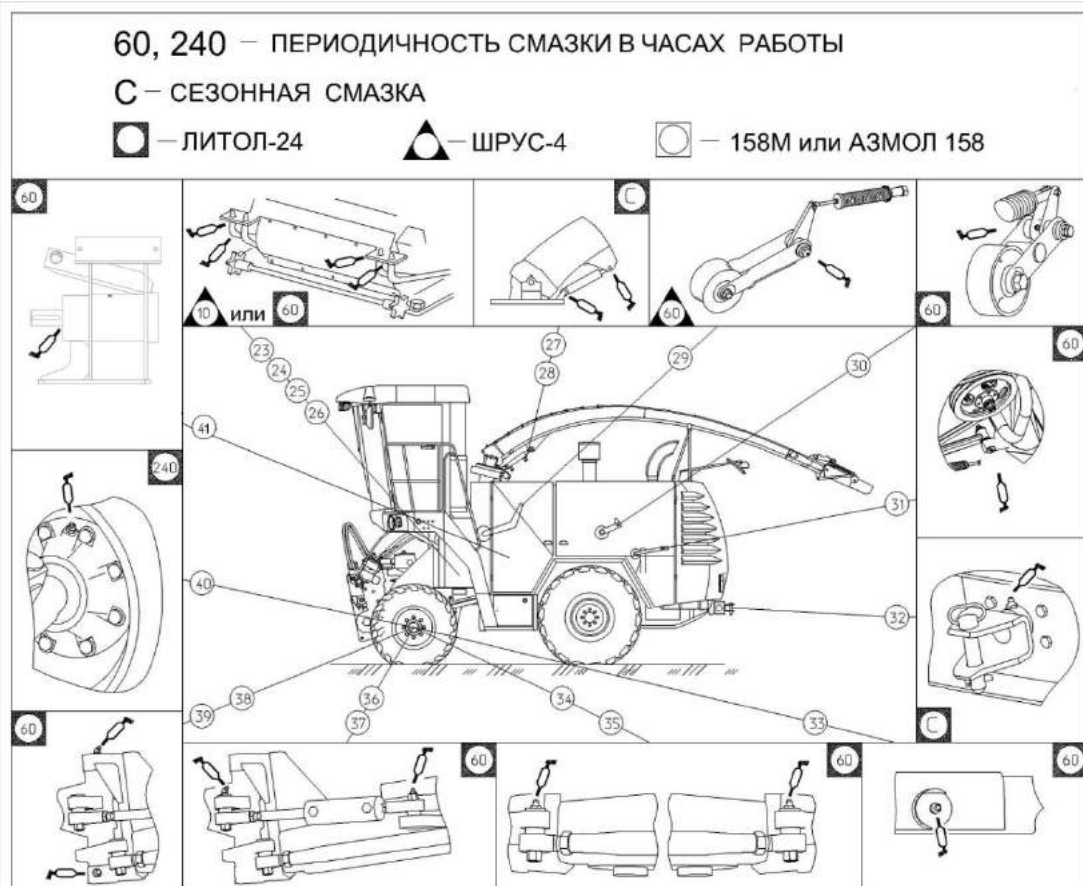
Схема смазки самоходного измельчителя (вид слева)
